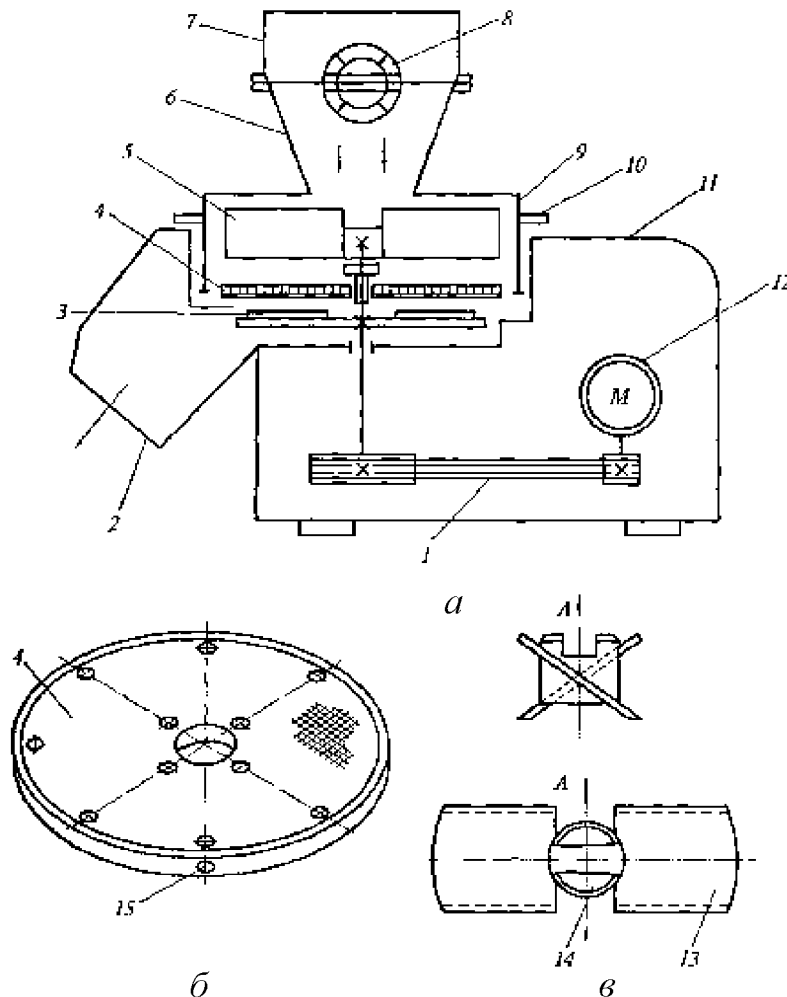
Протирально-різальна машина МПР-350: а – принципова схема; б – диск протиральний; в – ротор лопатевий; 1 – передача клинопасова; 2 – лотік розвантажувальний; 3 – скидач; 4 – диск протиральний (сито); 5 – ротор лопатевий; 6 – чаша конічна; 7 – обичайка; 8 – запобіжник; 9 – робоча камера; 10 – штифт; 11 – корпус; 12 – електродвигун; 13 – лопаті; 14 – втулка; 15 – гвинт
